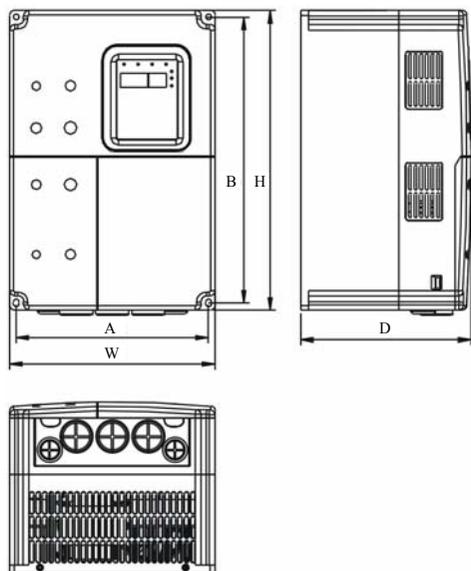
Габаритные и установочные размеры блоков торможения 380 В, 7,5 - 22 кВт
